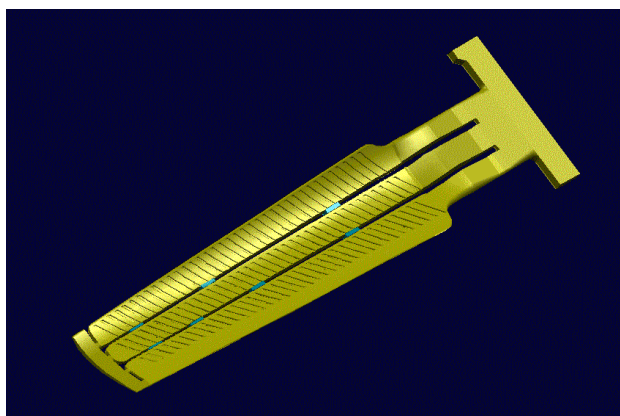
Turbína leteckého motoru typ PW4000-112, firma PRATT & WHITNEY [24]
